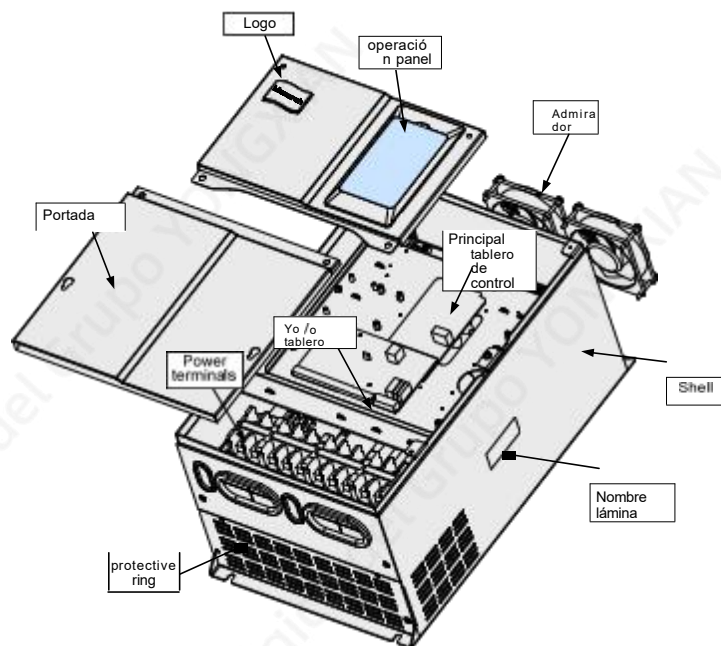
Vista en despiece de la estructura de chapa metálica (18,5–30 kW)
